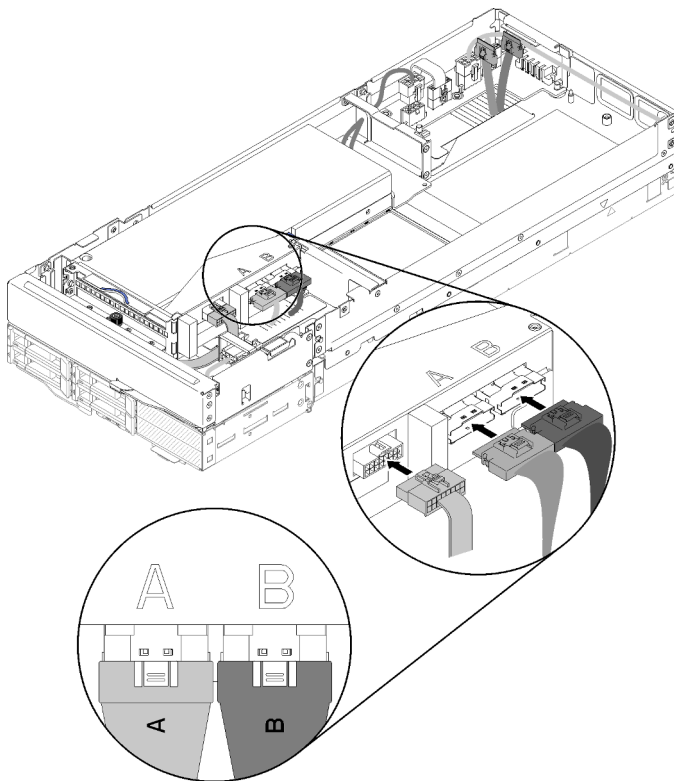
Connexion du câble PCIe#3-A, PCIe#4-B et du câble à usage divers de carte mezzanine à l'assemblage de cartes mezzanines avant
